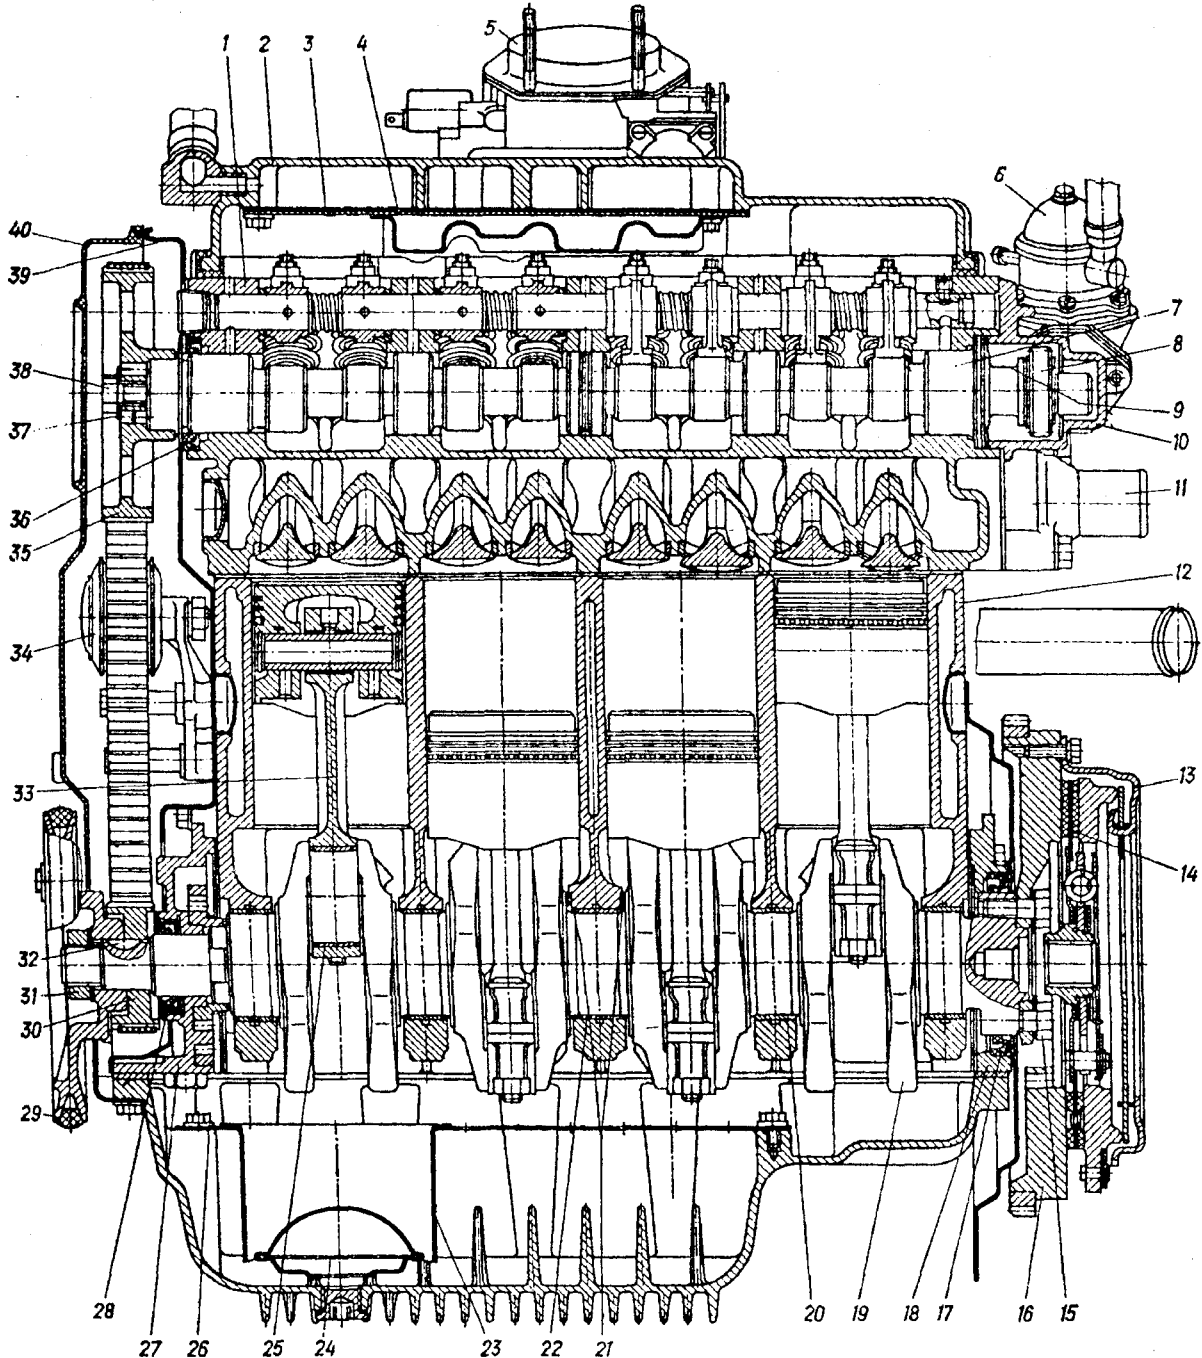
Продольный разрез двигателя: 1 – головка цилиндров; 2 – крышка головки цилиндров; 3, 4 – прокладка и крышка маслоотделителя; 5 – фланец карбюратора для крепления воздушного фильтра; 6 – бензиновый насос; 7 – вал распределительный; 8 – ведущая шестерня привода датчика-распределителя; 9 – кулачок привода бензинового насоса; 10 – корпус привода датчика-распределителя и бензинового насоса; 11 – отводящий патрубок; 12 – блок цилиндров; 13 – нажимной диск сцепления; 14 – диск сцепления ведомый; 15, 38 – болты; 16 – маховик; 17, 28, 36 – манжеты; 18 – держатель манжеты; 19 – коленчатый вал; 20 – вкладыши коренных подшипников коленчатого вала; 21 – упорные полукольца коренного подшипника коленчатого вала; 22 – вкладыш среднего коренного подшипника коленчатого вала; 23 – маслоуплотнитель; 24 – приемник масляного насоса; 25 – вкладыш нижней головки шатуна; 26 – масляный картер; 27 – масляный насос; 29 – шкив привода генератора; 30 – ведущий шкив коленчатого вала; 31 – гайка; 32 – шпонка; 33 – шатун с поршнем, поршневыми кольцами и пальцем; 34 – натяжной ролик; 35 – шкив привода распределительного вала; 37 – стопорная шайба; 39, 40 – внутренний и наружный кожухи зубчатого ремня
